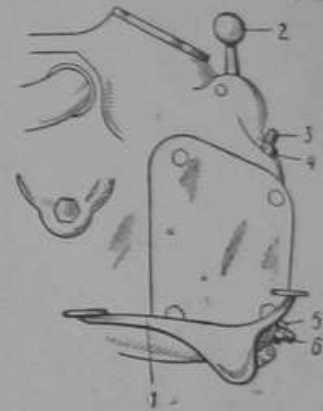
Эксплуатационная регулировка коробки передач: 1 — педаль ножного переключения передач; 2 — рычаг ручного переключения передач; 3 — регулировочный винт включения низших передач; 4, 5 — контргайки; 6 — регулировочный винт включения высших передач
